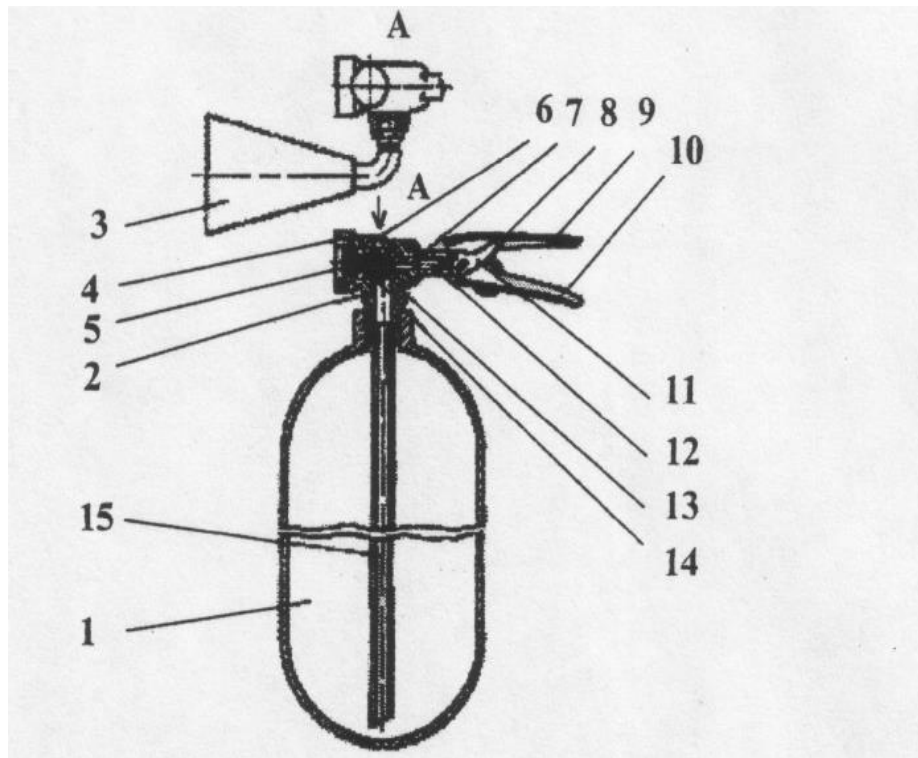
Вогнегасник ОУ-51 - корпус; 2 - головка; 3 - розтруб; 4 - гайка; 5 - запобіжна мембрана; 6 - шайка; 7 - кільце ущільнювальне; 8 - запобіжна чека; 9 - важіль керування клапаном; 10-ручка; 11 -кулачок; 12-шток; 13-клапан; 14-пружина; 15 - трубка сифонна.
